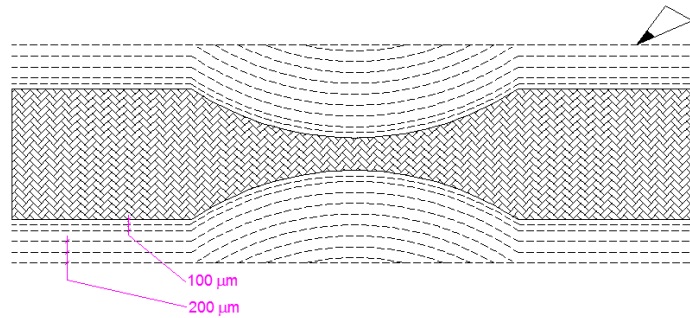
Schéma d'usinage pour l'éprouvette
